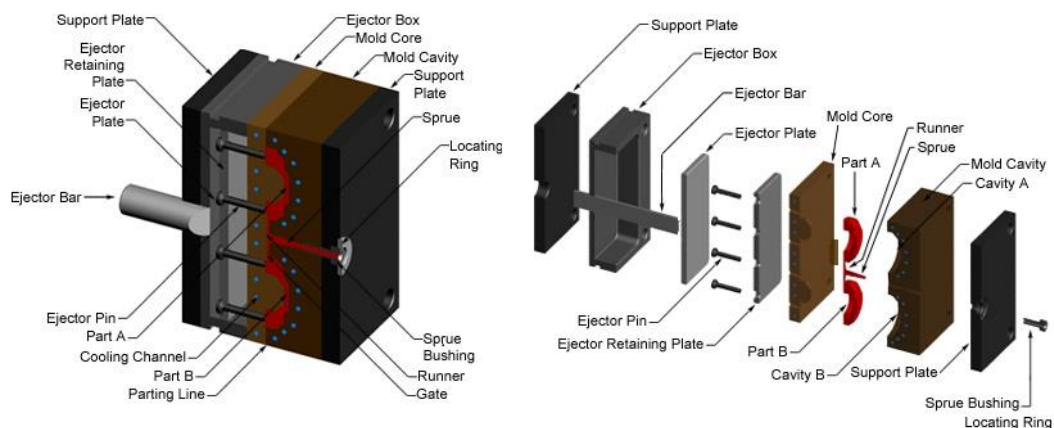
Constituição elementar de um molde de injeção [3].
